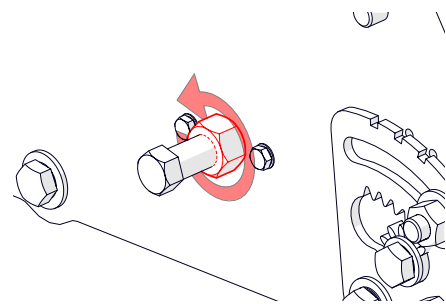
A – Kontermutter der Befestigungsschraube lösen
